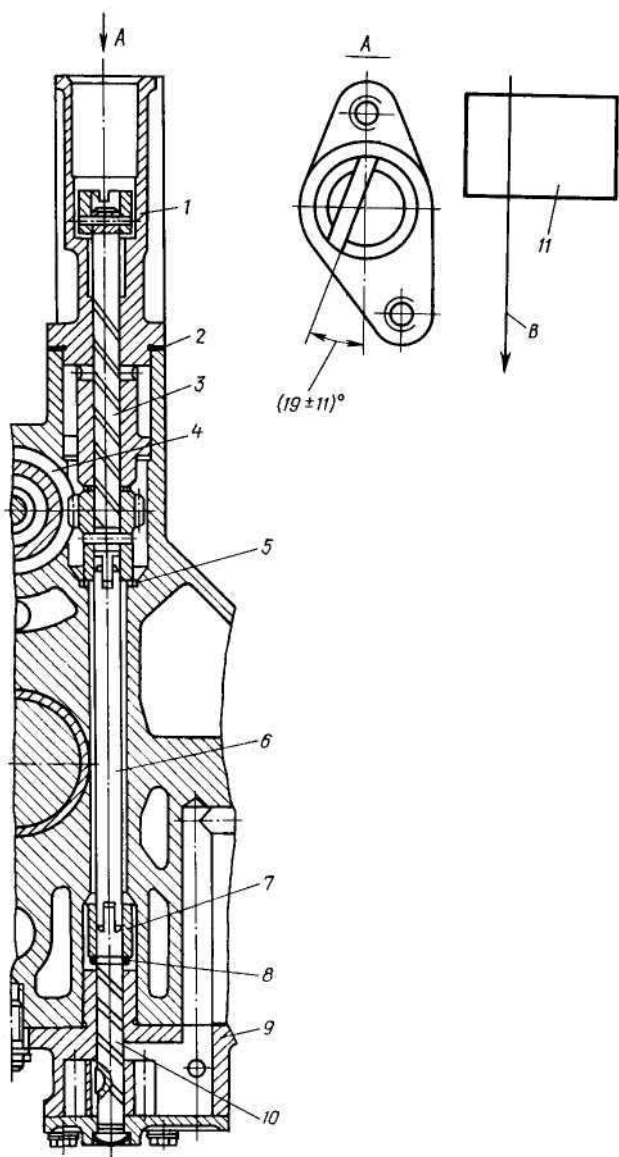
Установка привода распределителя зажигания: 1 — привод распределителя зажигания; 2 — прокладка; 3 — валик привода распределителя; 4 — ведущая шестерня привода распределителя зажигания; 5 — шайба; 6 — валик промежуточного привода масляного насоса; 7 — втулка промежуточного масляного насоса; 8 — стопорное кольцо; 9 — масляный насос; 10 — ведущий валик масляного насоса; 11 — масляный радиатор; B — ось коленчатого вала
